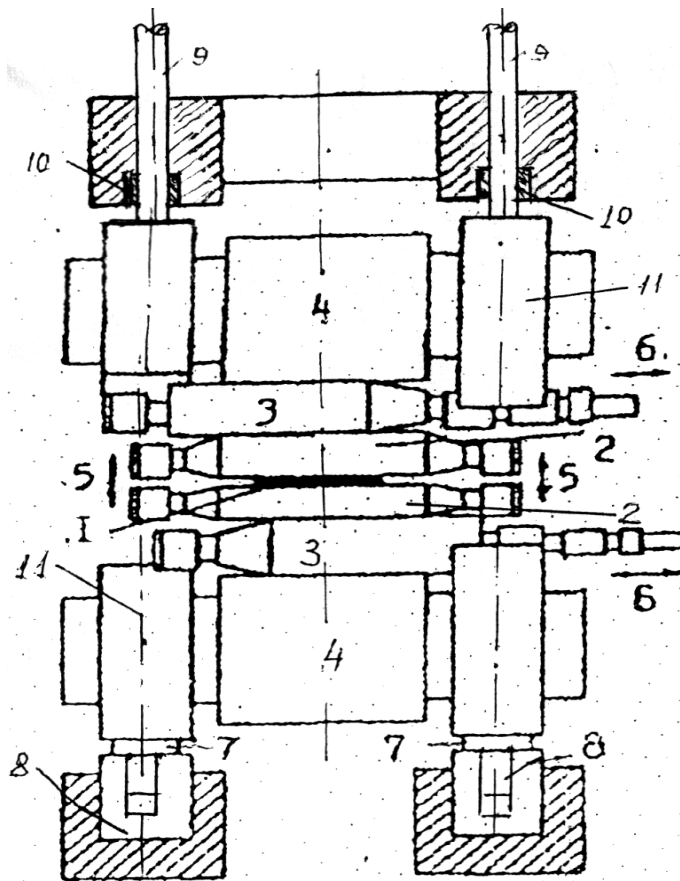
Схема шестивалкової кліті НС: 1 – штаба; 2 – робочі валки; 3 – проміжні валки; 4 – опорні валки; 5 – напрям вигину робочих валків; 6 – напрям осьового переміщення; 7 – мес дози; 8 – нижні гідро натискні устрої; 9; 10 – гвинт і гайка верхнього натискного устрою; 11 - станини
